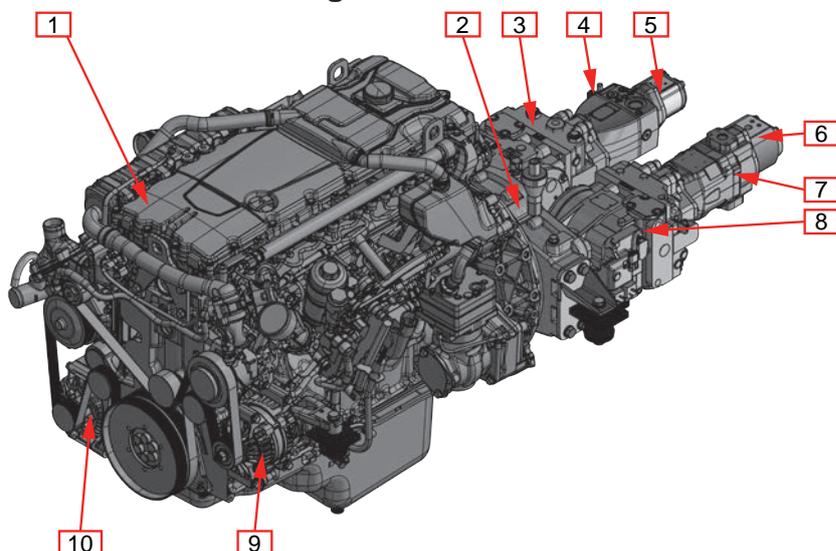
Motor und Hydraulikpumpen DT 2400H
